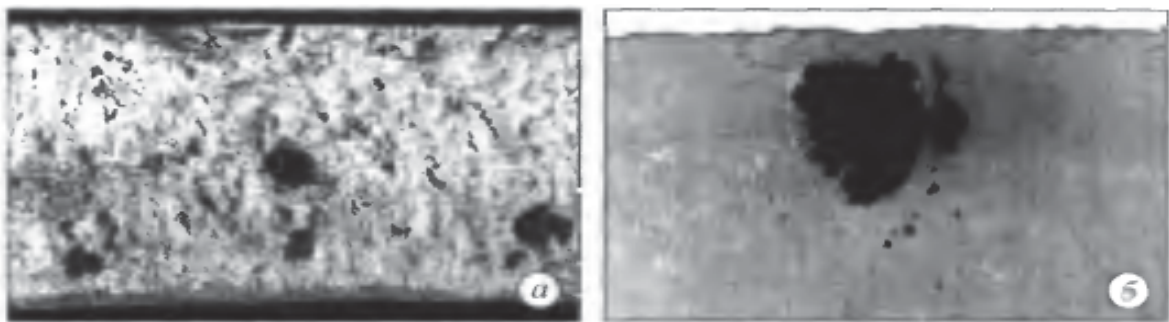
Шлаковые включения в сварном шве (сталь):
